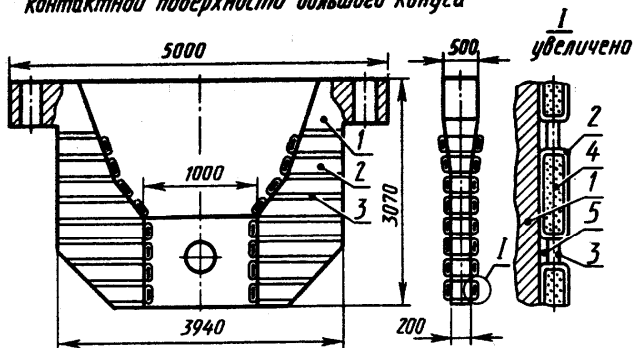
Схема армирования плоскими трубами подвески большого конуса
